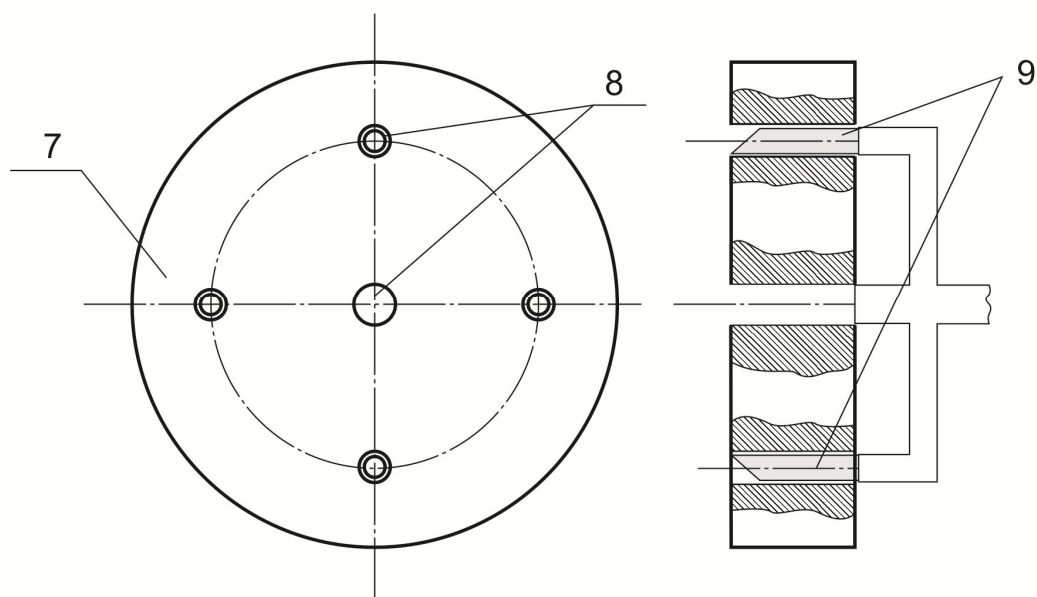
б - Неподвижный жернов с напороустойчивыми трубками
